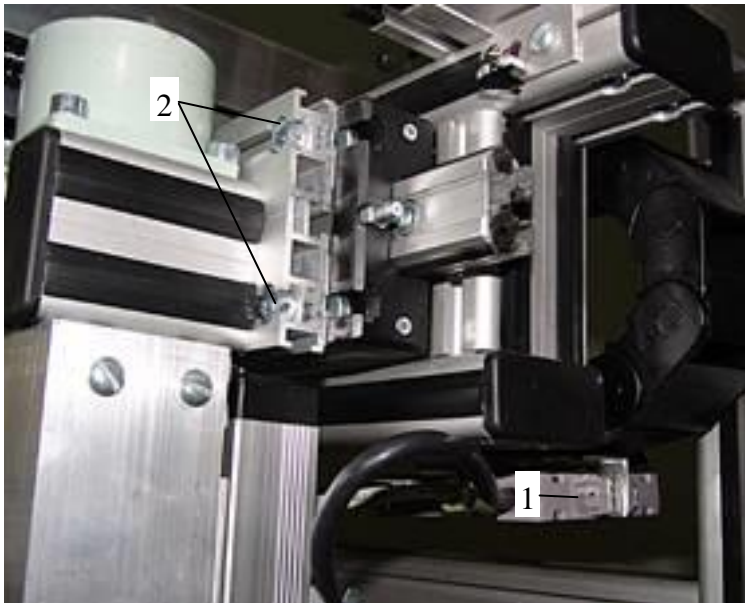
Крепление привода Z станка «График-ЗК».
